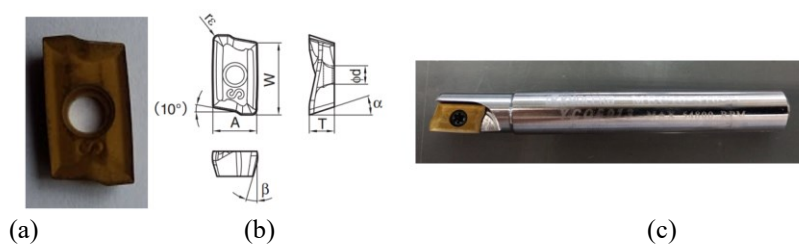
(a) Geometria do inserto. (b) Desenho do inserto. (c) Exemplo de montagem do inserto e suporte MEC10-S10-11 utilizado
